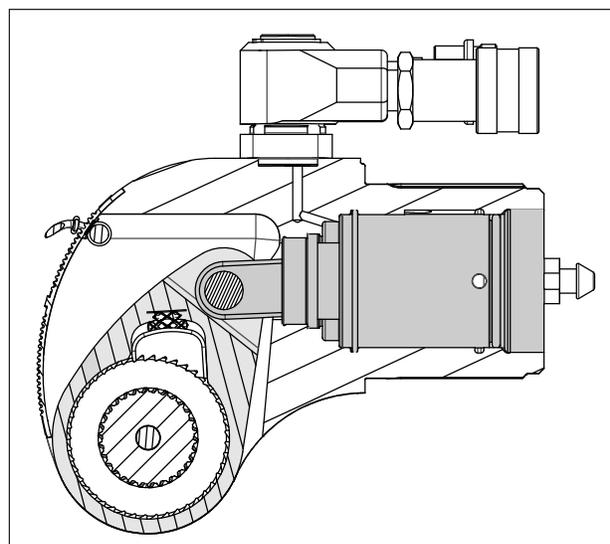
Vue en coupe du positionnement du piston et de la plaque du carré conducteur
